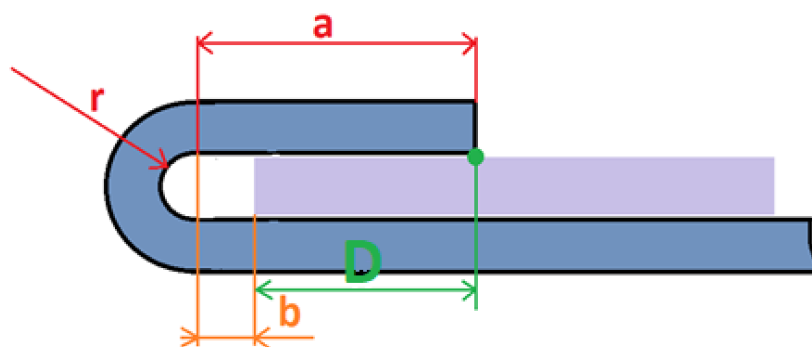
Detailní pohled na pozici drážkové fixace sesazených dílů před lemováním [P12]
